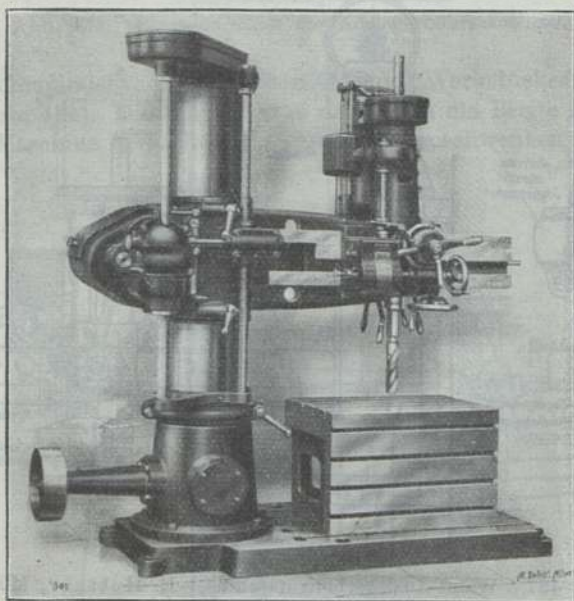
Auslegerbohrmaschine. H. Hessenmüller, Ludwigshafen.
